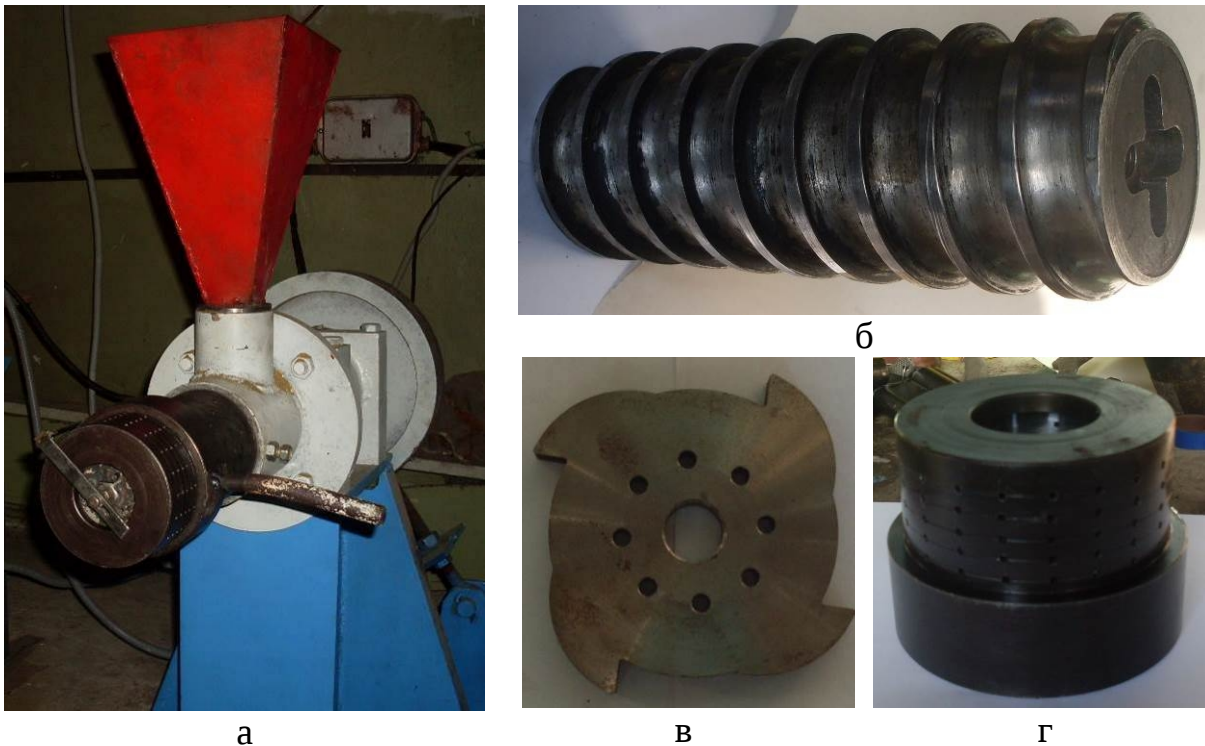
Експериментальний зразок установки для виготовлення пелет (пелетератора): а – загальний вигляд; б – гвинт; в – формуючий кулачок; г – циліндрична матриця
